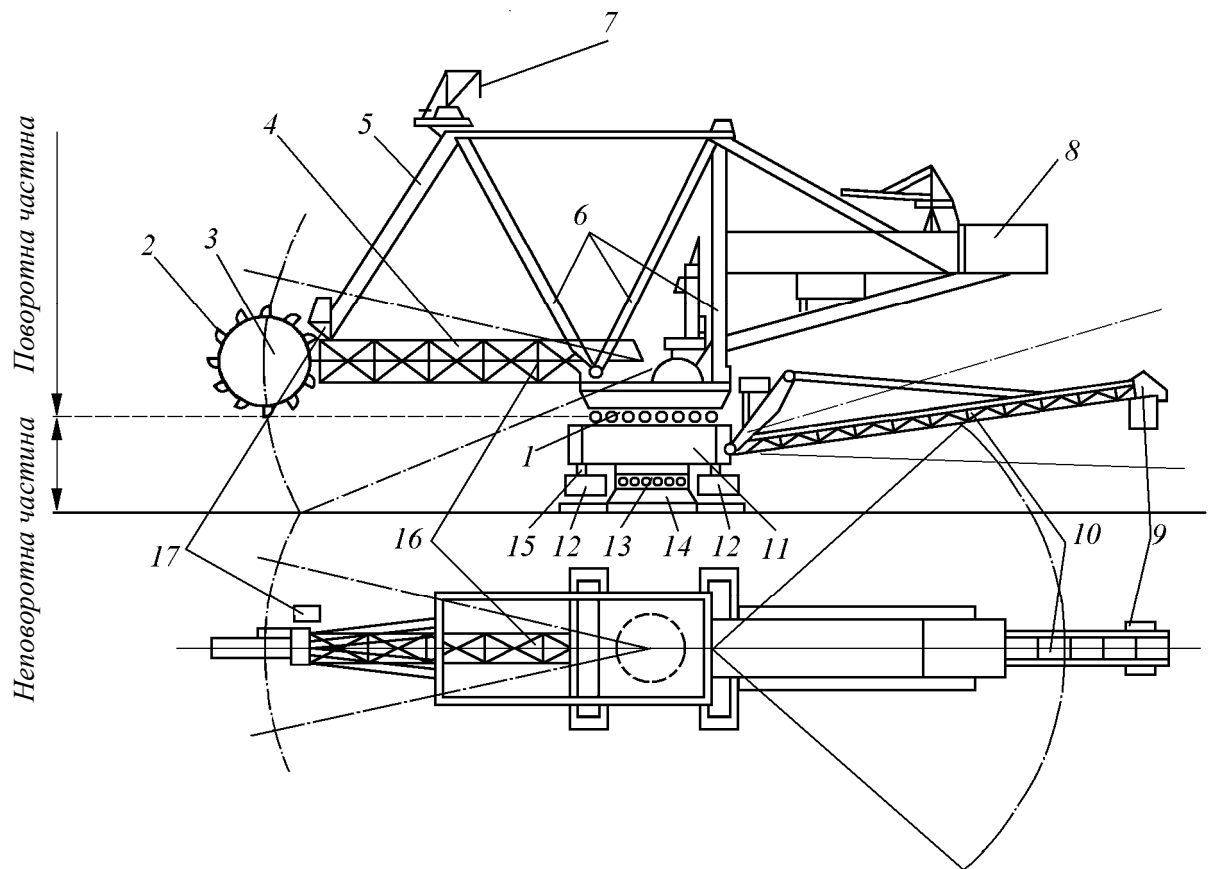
Компонувальна схема роторного екскаватора
